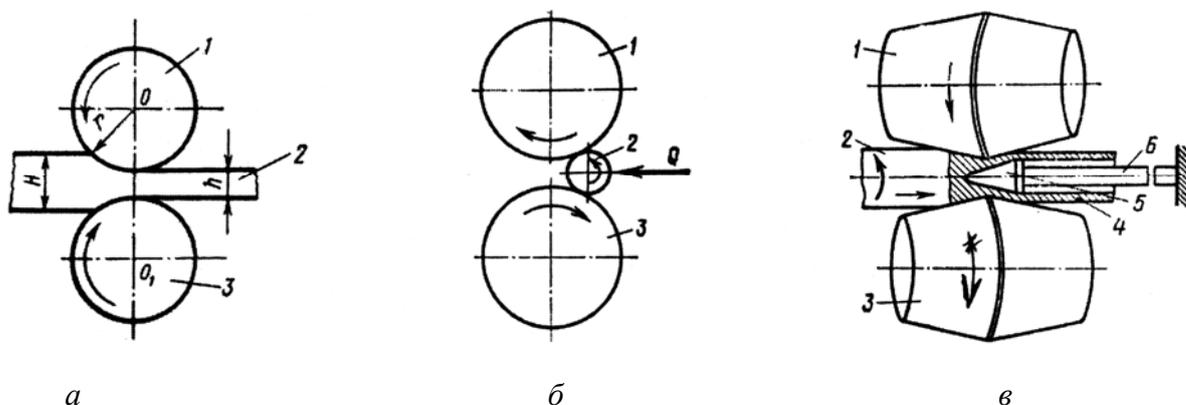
Схемы прокатки: а – продольная; б – поперечная; в – поперечно-винтовая: 1 – правый валок; 2 – заготовка; 3 – левый валок; 4 – гильза; 5 – оправка; 6 – штанга (стержень)
